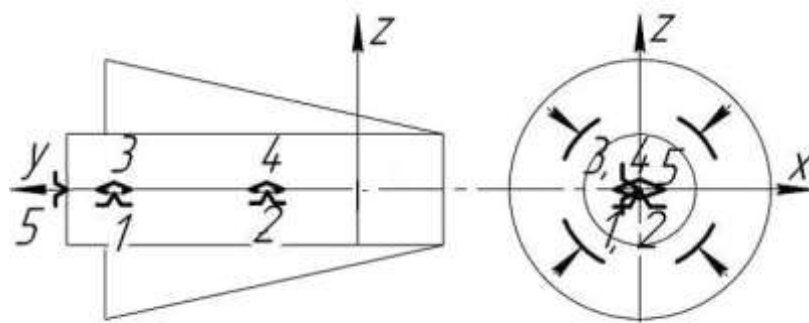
Установка вала в цанговом патроні токарно-револьверного автомата.
